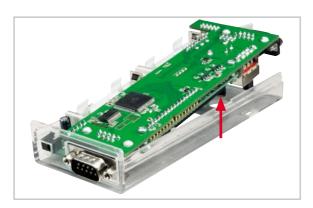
Die SDSD1-Elektronikeinheit wird für die Montage über Kopf von schräg oben zuerst in die stirnseitigen Fräsungen der Gehäuseoberseite gesteckt. Nur so passt auch die mit dem Pfeil gekennzeichnete Dreh-Drück-Schalter-Achse durch die runde Fräsung.
